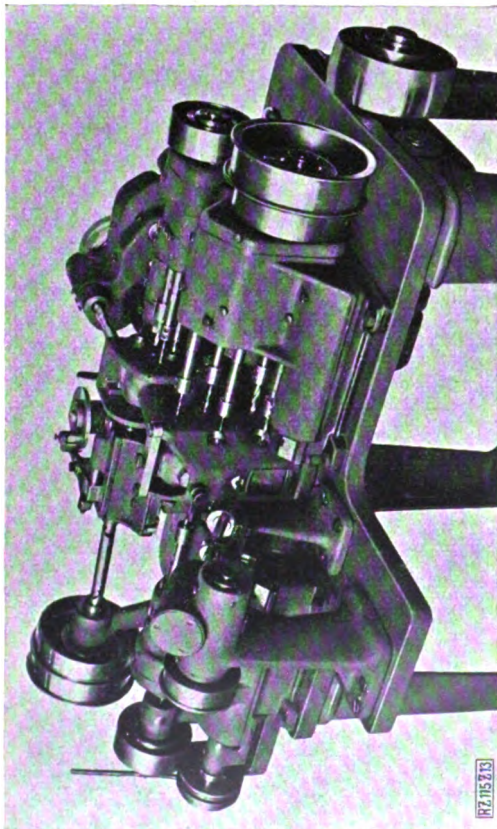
Maschine für die dritte Arbeitsstufe am Nähmaschinenarm
